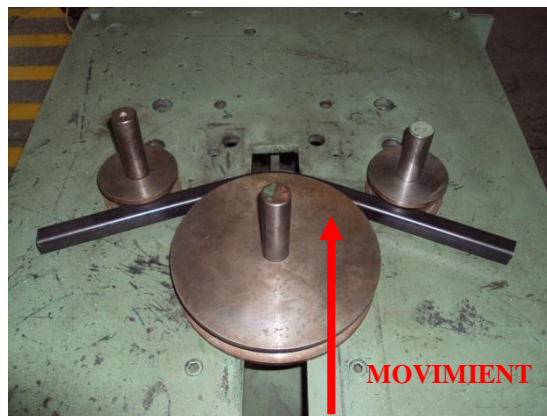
Probeta de tubo cuadrado durante el proceso de doblado
